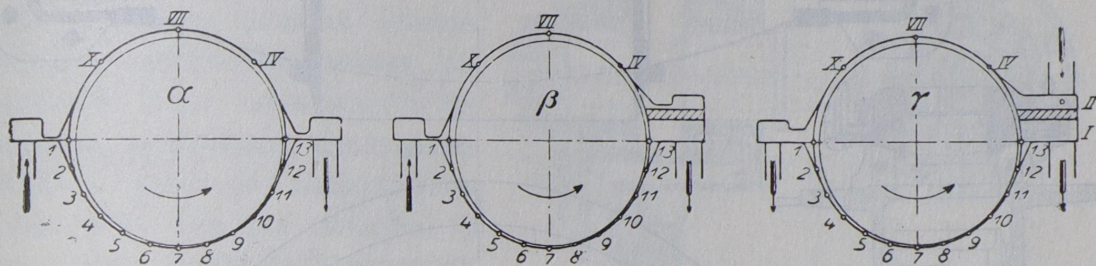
304. Развитие конструкции вкладыша подшипника.
